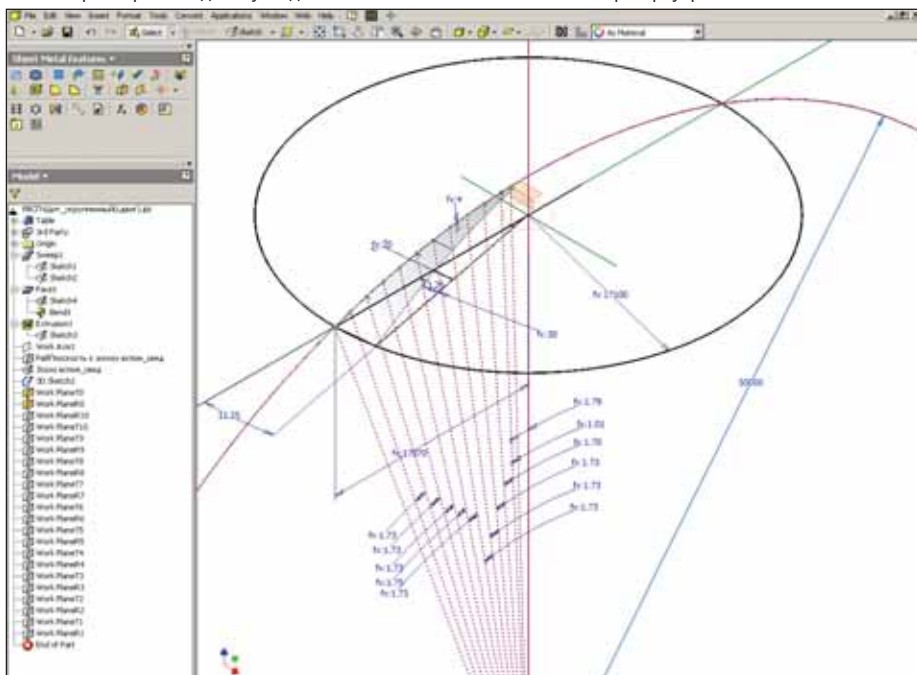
Модель укрупненного щита сферической крыши резервуара с набором вспомогательных плоскостей для соединения в модуле сборки с поперечными элементами конструкции (уголки)
